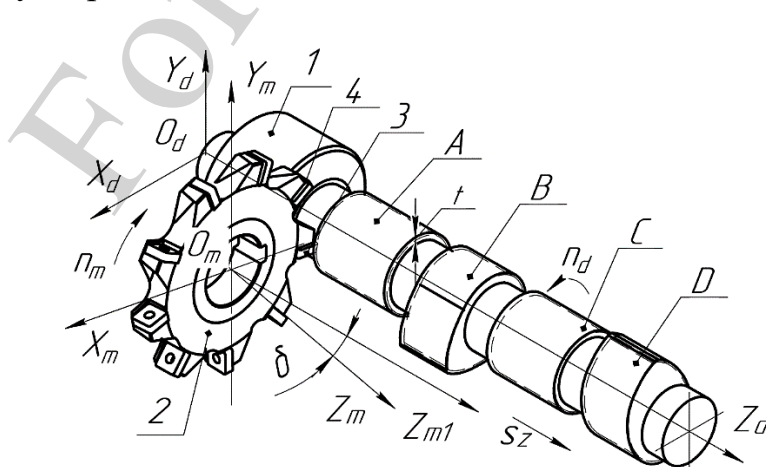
Схема фрезерування розподільного валу зі схрещеними осями інструмента та деталі
